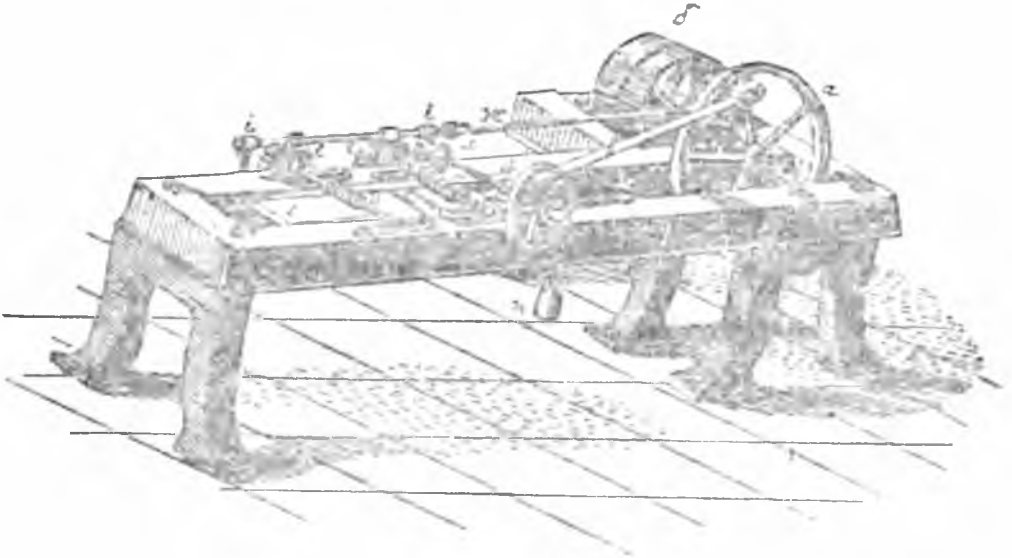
й. Машина простого действия: а—маховое колесо; б—два шкива—рабочий и холостой; в—шатуны; г—салазки, с укрепленными в них резами и строгальным ножом; д—два вальца; е—зубчатки на концах валцов; ж—штанга для передачи движения от рабочего вала вальцам; з—винтовая нарезка на валу, скрепляющаяся с зубчаткой на конце штанги; и—ось с винтовой нарезкой; к—две зубчатые рейки, на которых укреплен передвижной валец; л—две полустержни, сцепляющиеся с зубчатыми рейками; м—рычаг для перемещения передвижного вальца; н—груз, подвешенный к ободу колеса с рычагом и служащий для натавливания передвижного вальца на перерабатываемый отрубок (последнего на рисунке не представлено).
